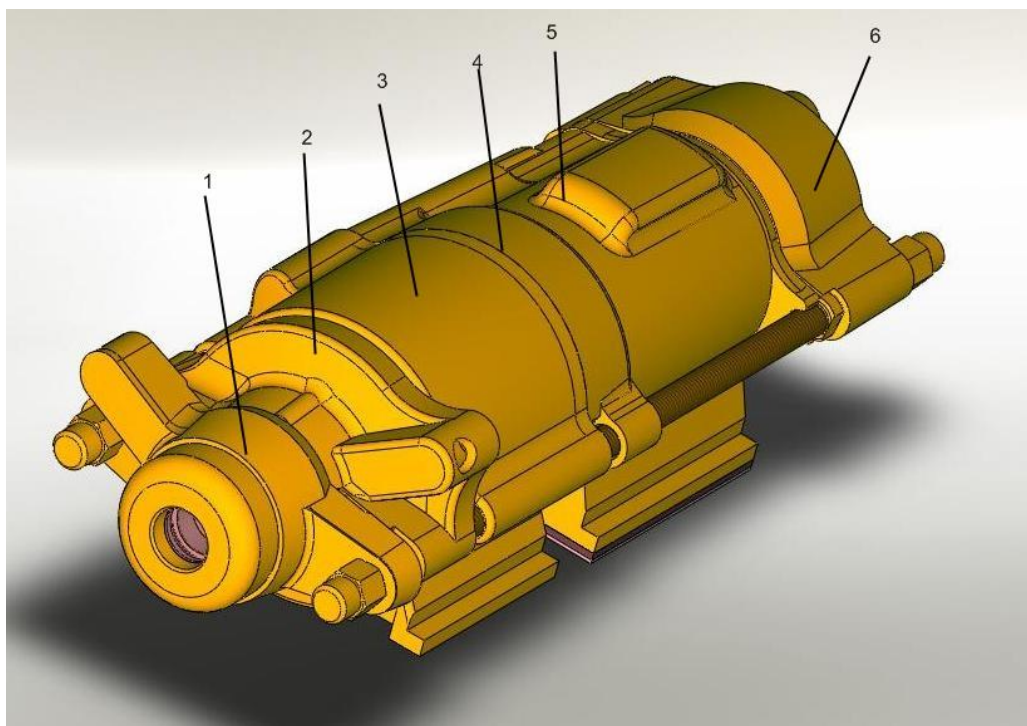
Основні вузли бурильної головки: 1 - кришка; 2 – кришка; 3 – корпус; 4 – корпус; 5 – корпус; 6 – кришка
